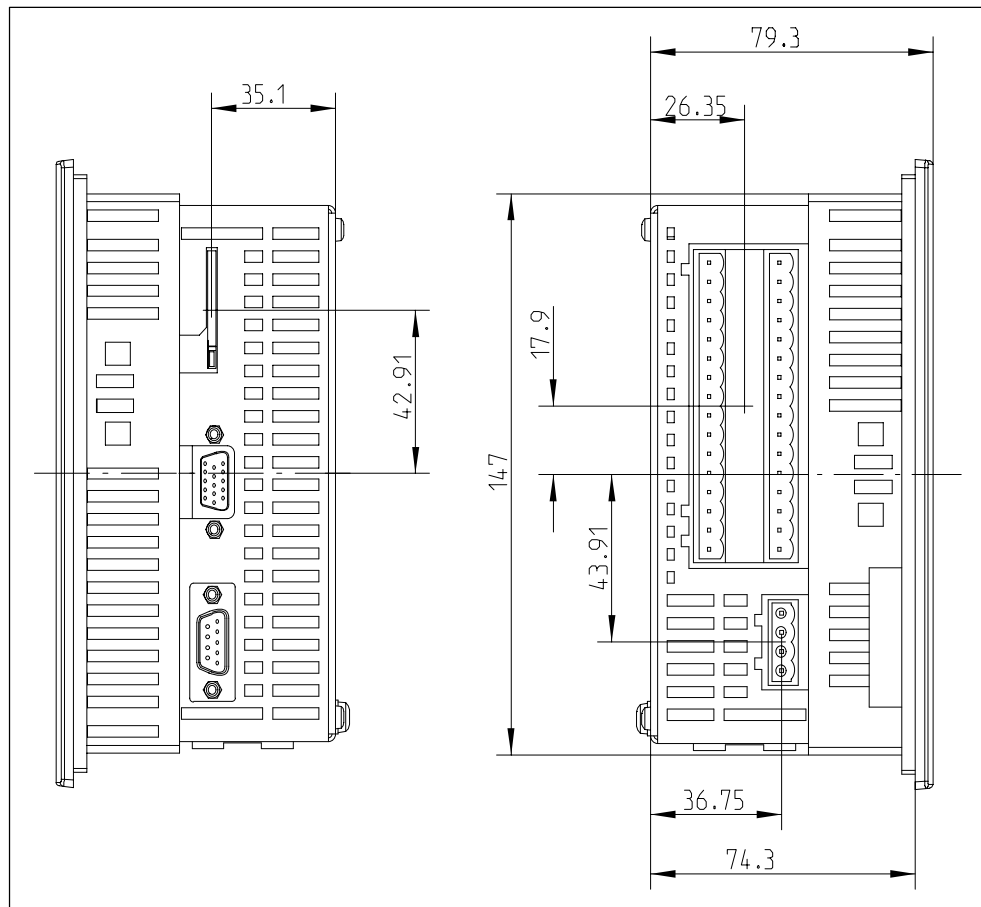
Maßbilder für das C7-613 (Maße in Millimeter)
